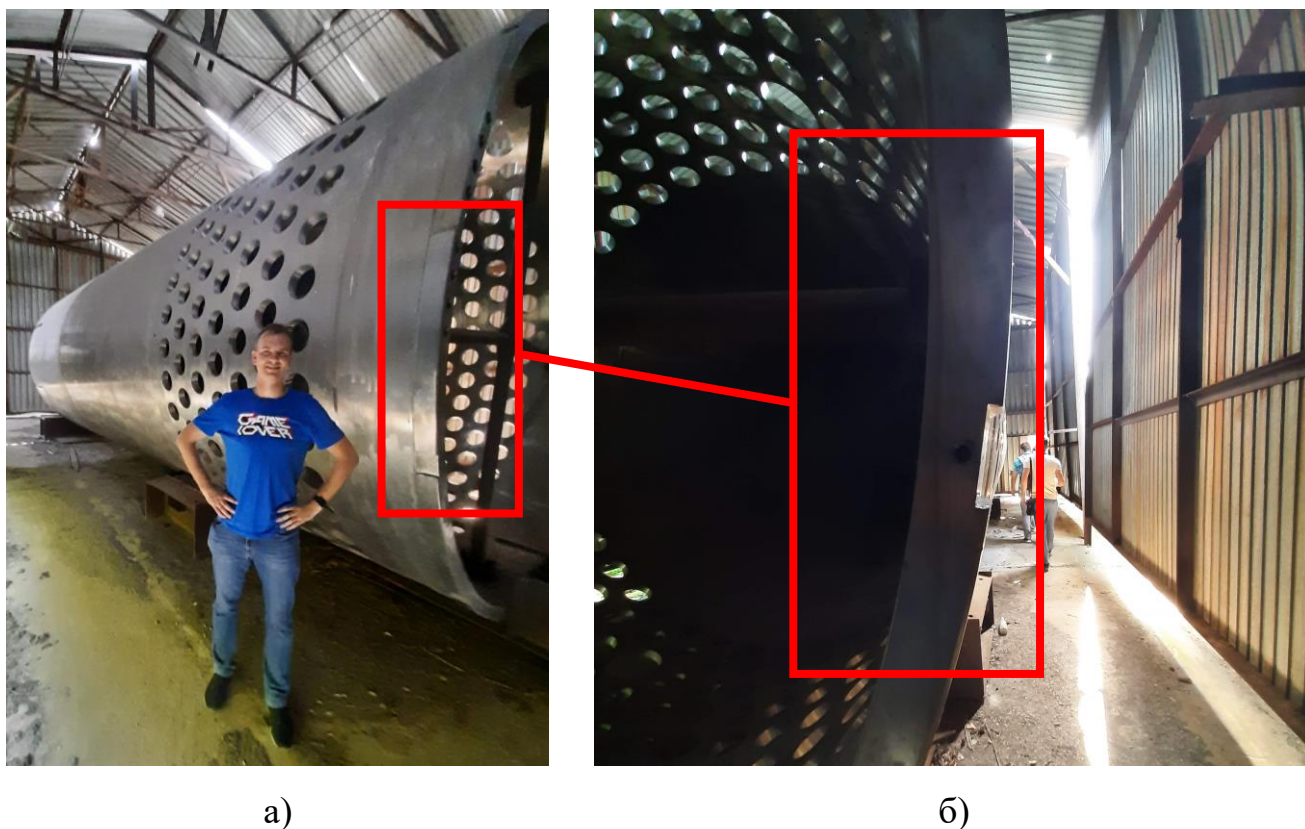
Загальний вигляд ШВК (а), вигляд частини ШВК зверху (б)
